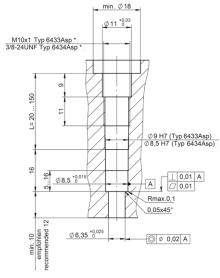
Bohrung für Einbau mit Montagehülse, kundenspezifisch
